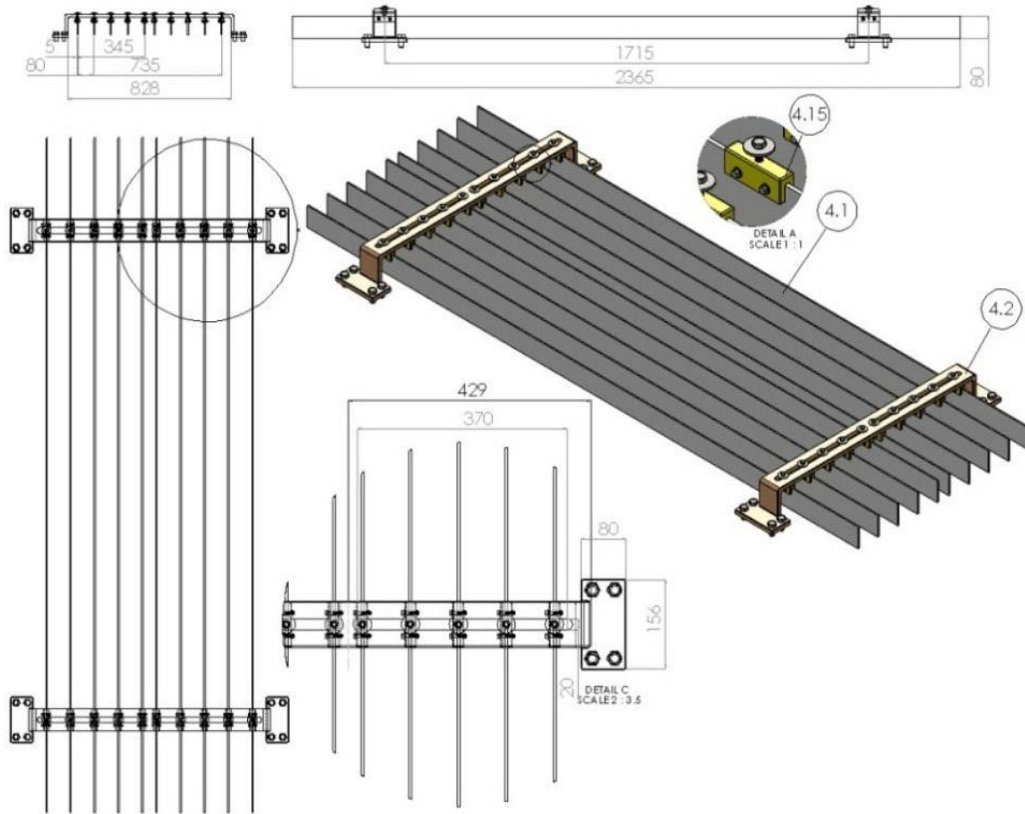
Şekillendirme tamburu (80 gram helva kalıbı için)
